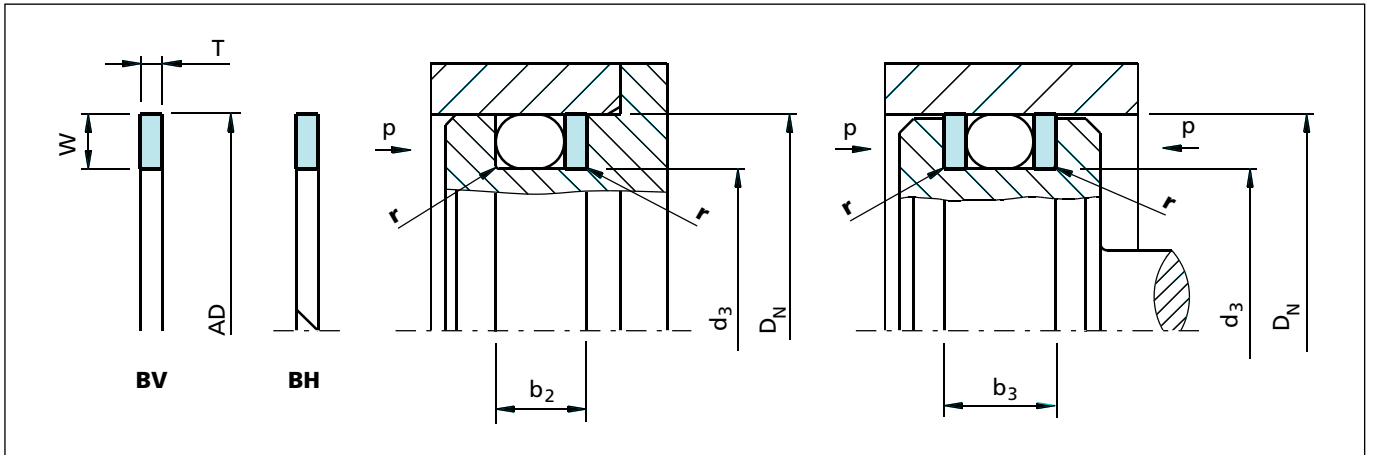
Einbauzeichnung außendichtend, rechteckige Stützring Bauformen
